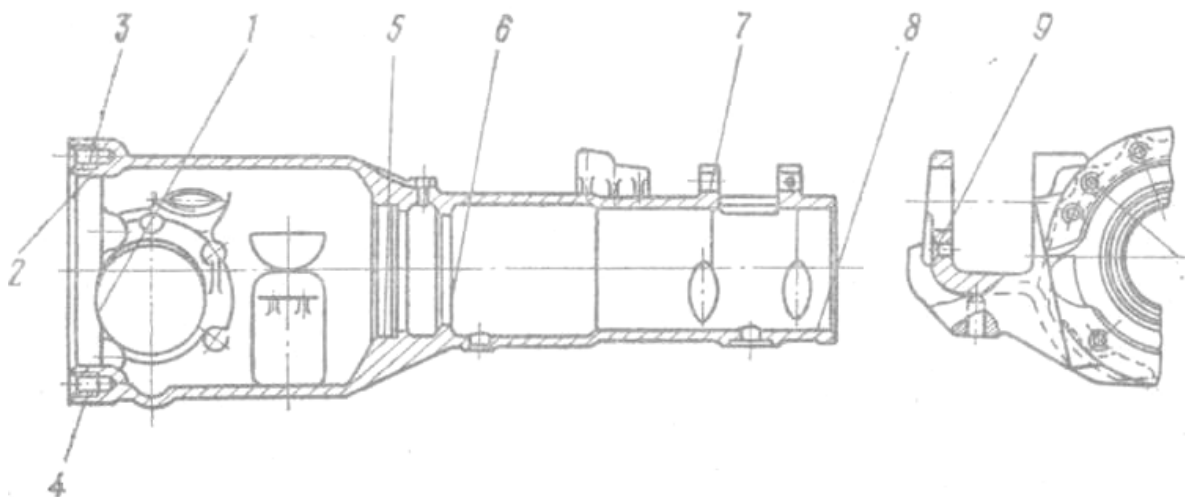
Корпус 52-2301055-А3. Матеріал — відливка 40Л; маса 36,2 кг; твердість — 143...217 НВ
